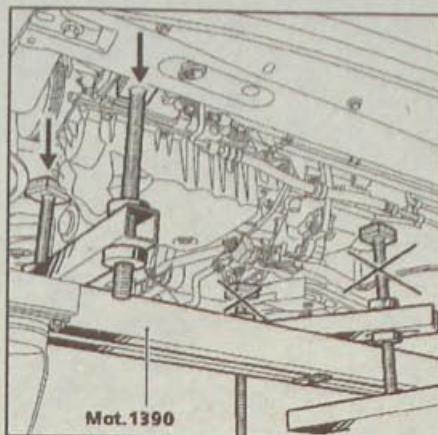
Установка правых башмаков универсальной опоры Mot. 1390 под силовой агрегат
